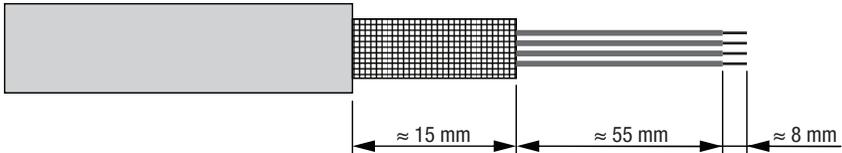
Confección del cable para la cubierta de bornes MK 304
